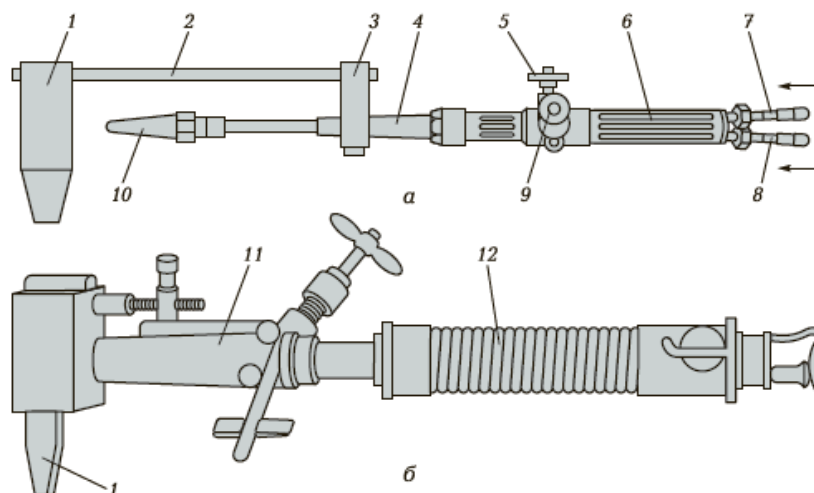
Паяльники непрерывного нагрева: а — газовый; б — бензиновый; 1 — рабочая часть; 2 — стержень; 3 — хомутик; 4 — горелка; 5, 9 — краны; 6 — рукоятка; 7, 8 — штуцеры; 10 — сопло; 11 — бензиновая горелка; 12 — рукоятка-резервуар
